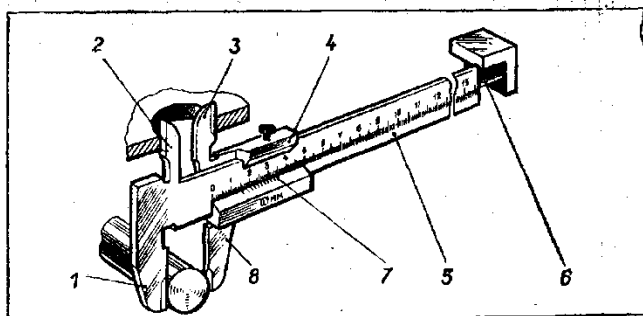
Штангенциркуль с точностью измерения до 0,1 мм:
